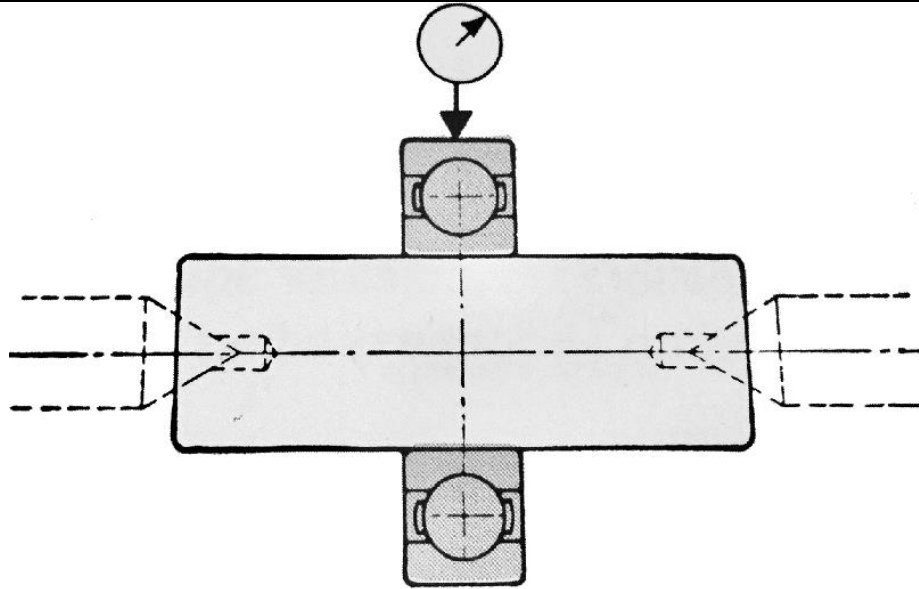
Измерение радиального биения внутреннего кольца радиальных шариковых и роликовых подшипников (кроме радиально-упорных подшипников). Измеряется путем установки подшипника на оправку. Наружное кольцо удерживается неподвижным, в то время как внутреннее кольцо (оправка) вращается на один полный оборот. Оправка имеет допуск на конусность!
